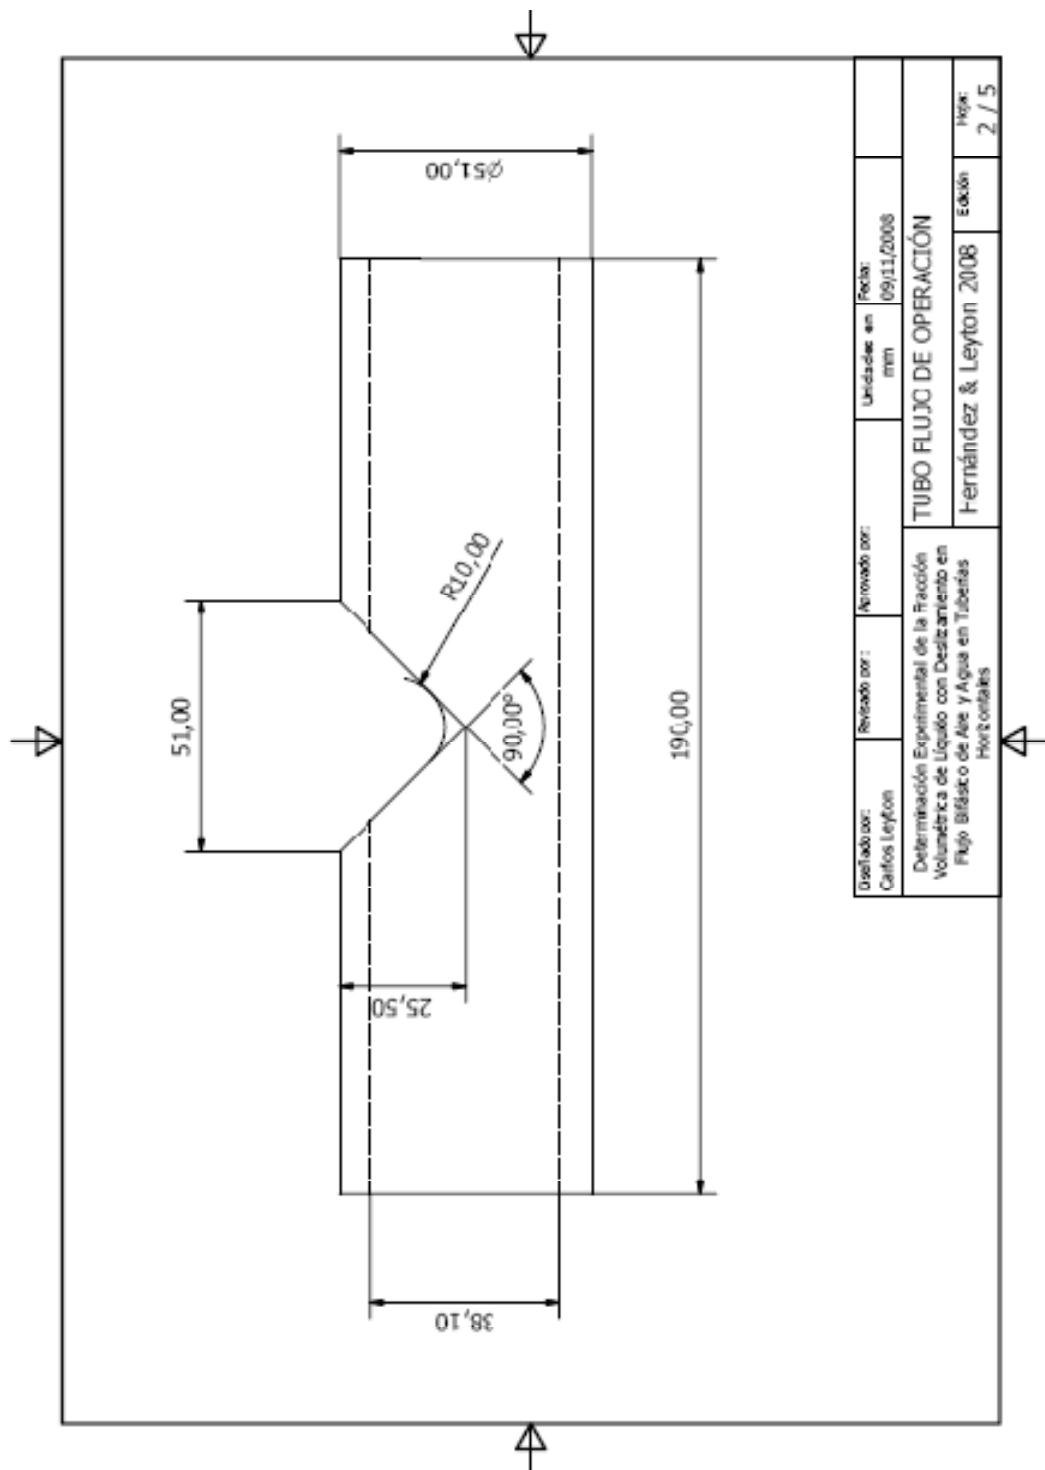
Planos constructivos de la Sección de desvío de flujo (2/5).
